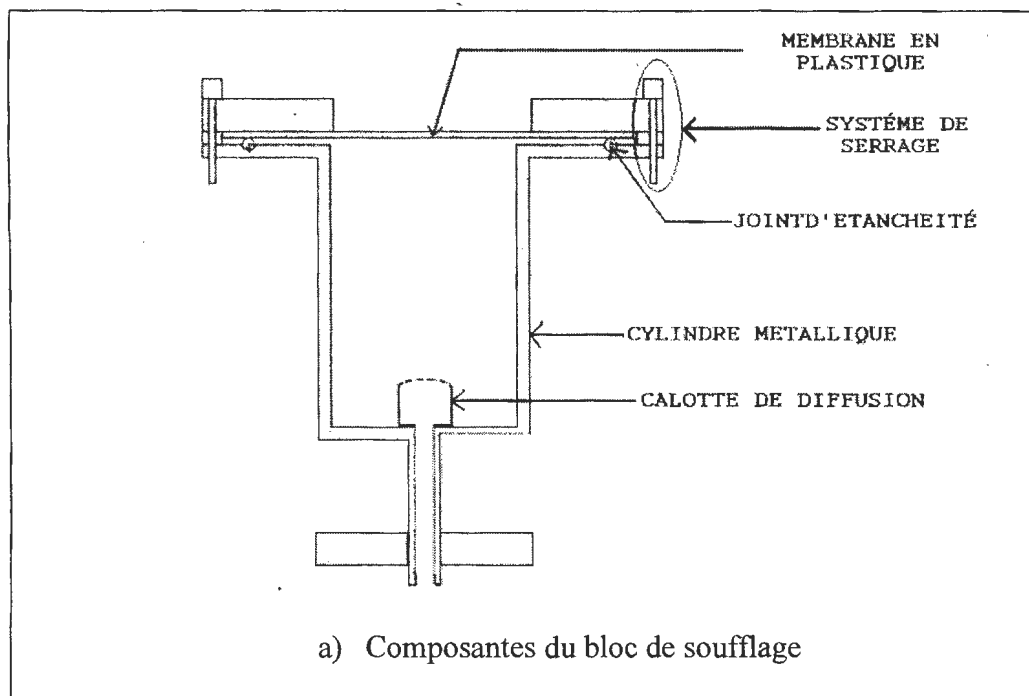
Vue d'ensemble du module de soufflage utilisé
